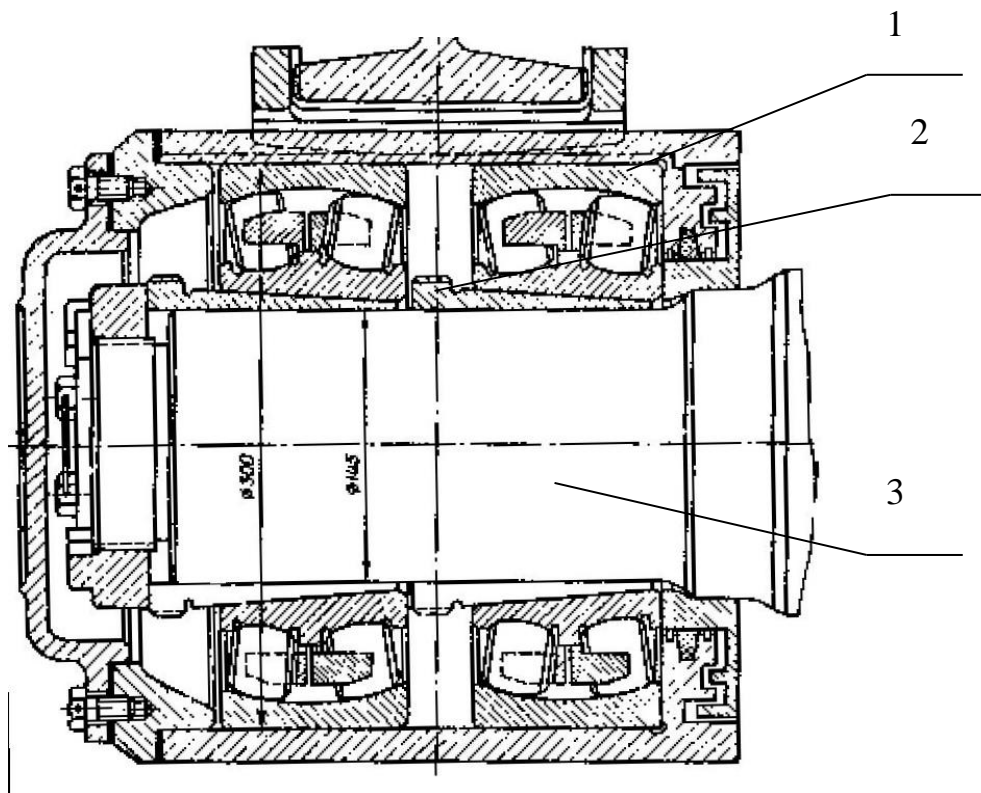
Буксовий вузол з двома сферичними підшипниками на втулковій посадці:
